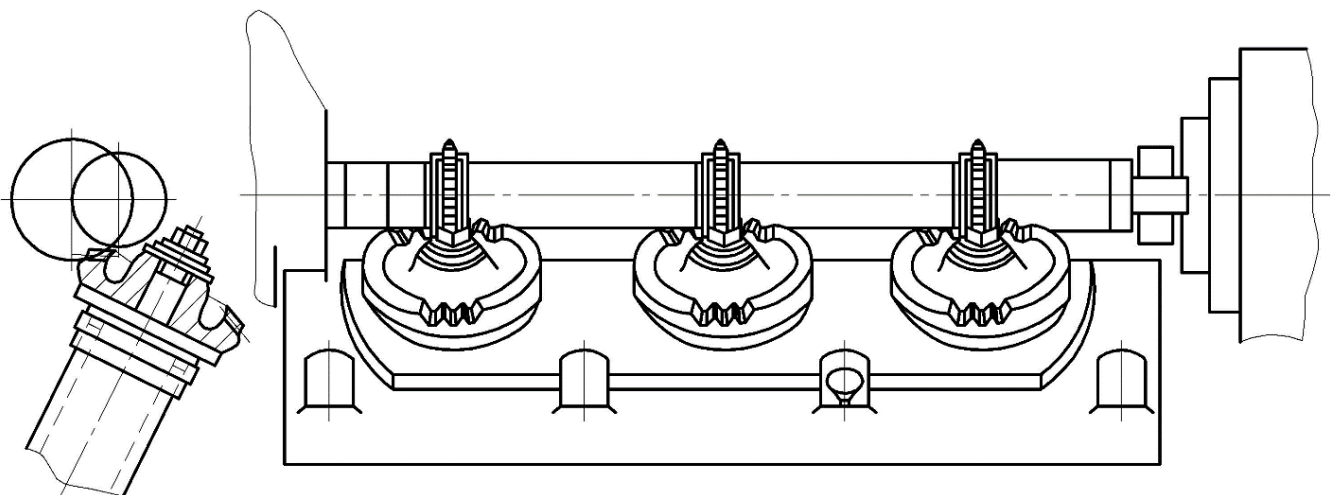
Попереднє фрезерування одночасно трьох заготовок конічних зубчастих коліс
